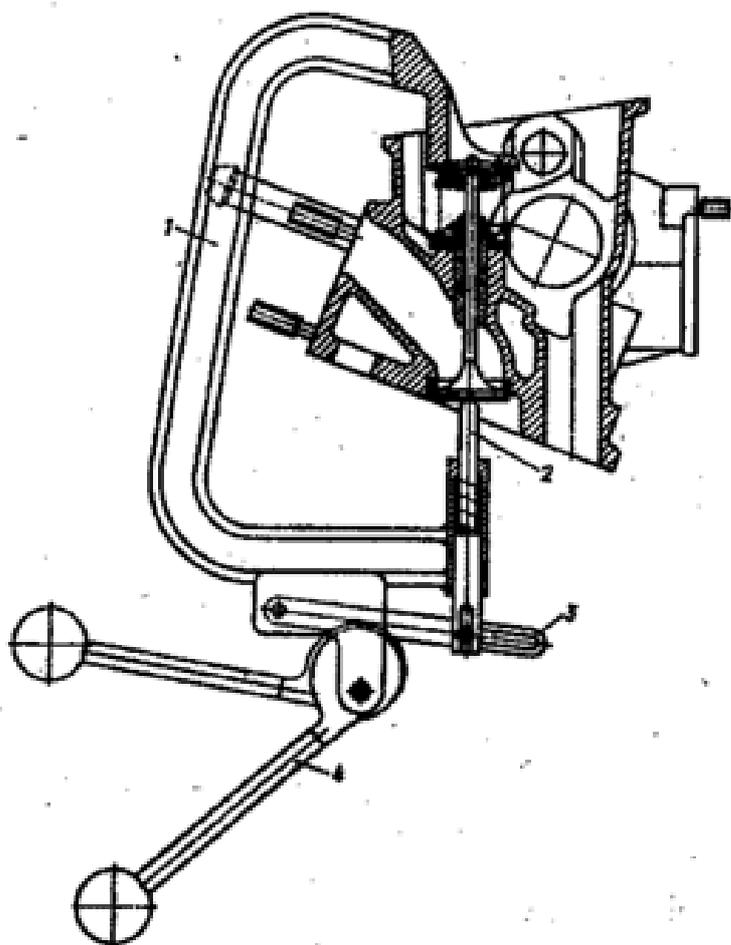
Приспособление М9832-386 для рассухаривания клапанов: 1 - скоба; 2 - шток; 3 - планка; 4 - рычаг с кулачком.
